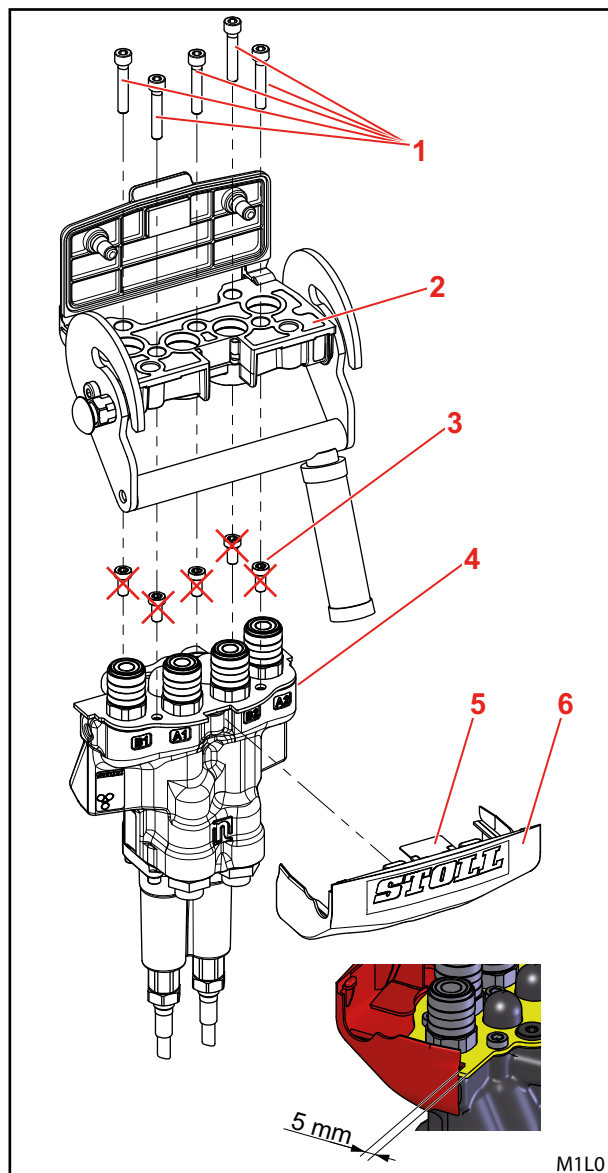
Установка нижнего узла Hydro-Fix на клапаны Нудас (без электрооборудования)
